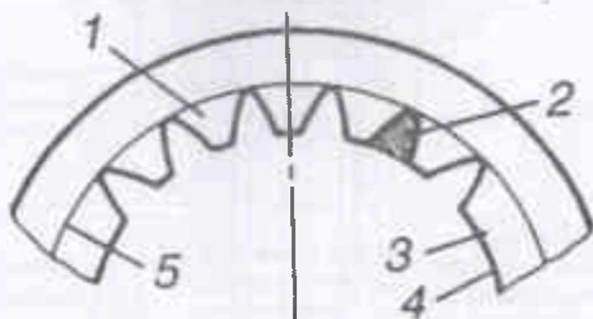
Елементи зубчастого колеса із внутрішніми зубцями: 1 – зуб; 2 – впадина; 3 – зубчастий вінець; 4 – поверхня вершин; 5 – поверхня впадин
